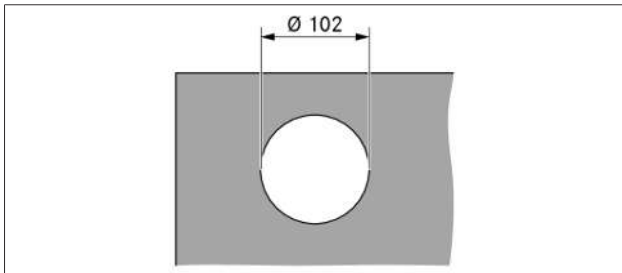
Dimensioni intaglio montaggio in battuta
